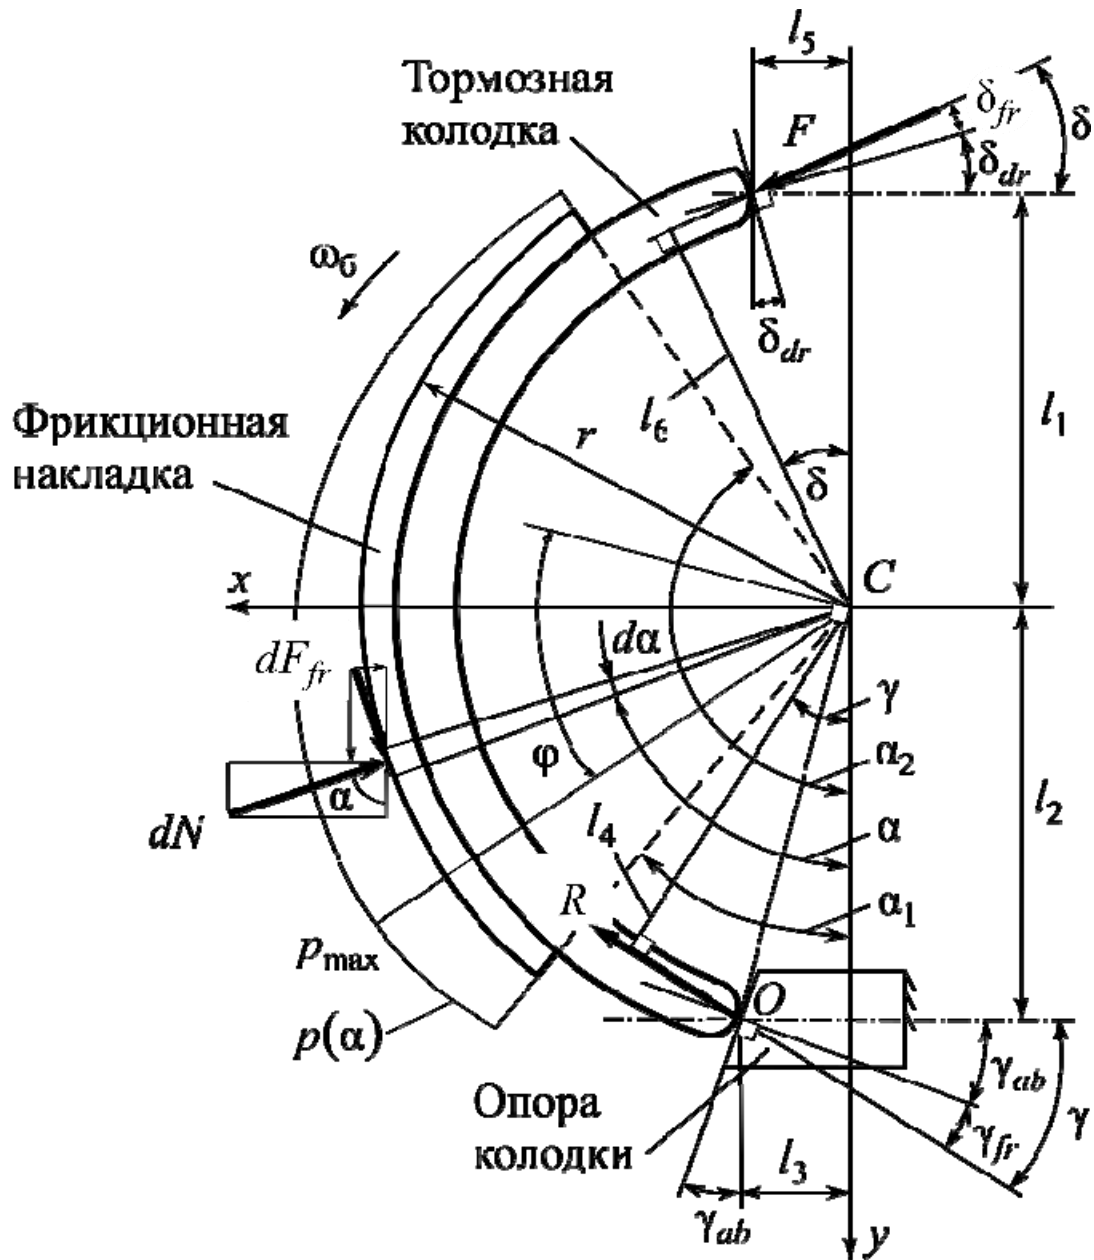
Расчетная схема ведущей колодки с плавающей опорой
